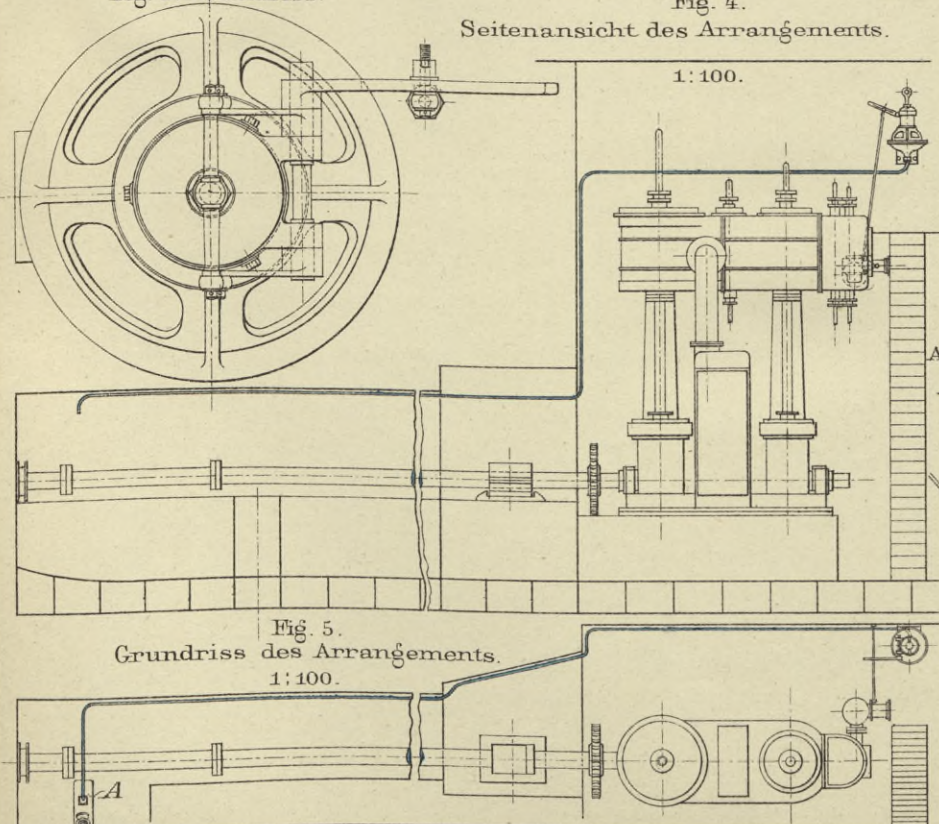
Grundriss des Arrangements. 1:100.
